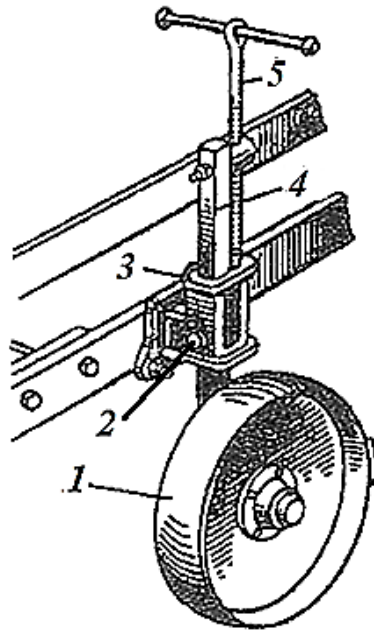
Гвинтовий механізм опорно-копіюючого колеса:
